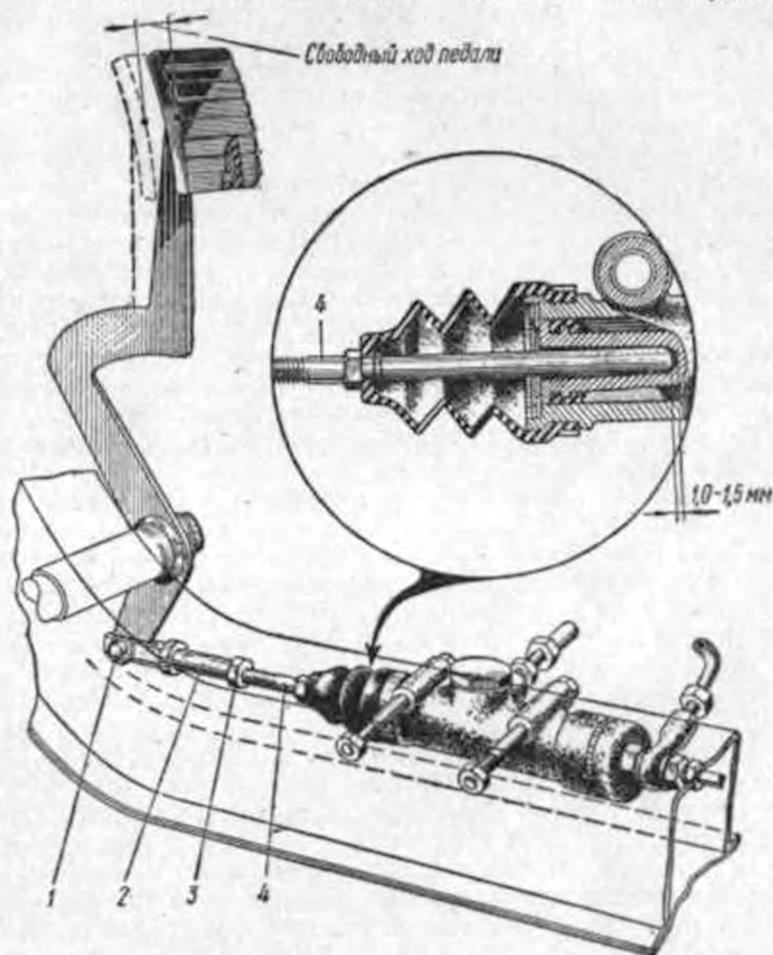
Регулировочный узел гидравлического привода ножного тормоза:
